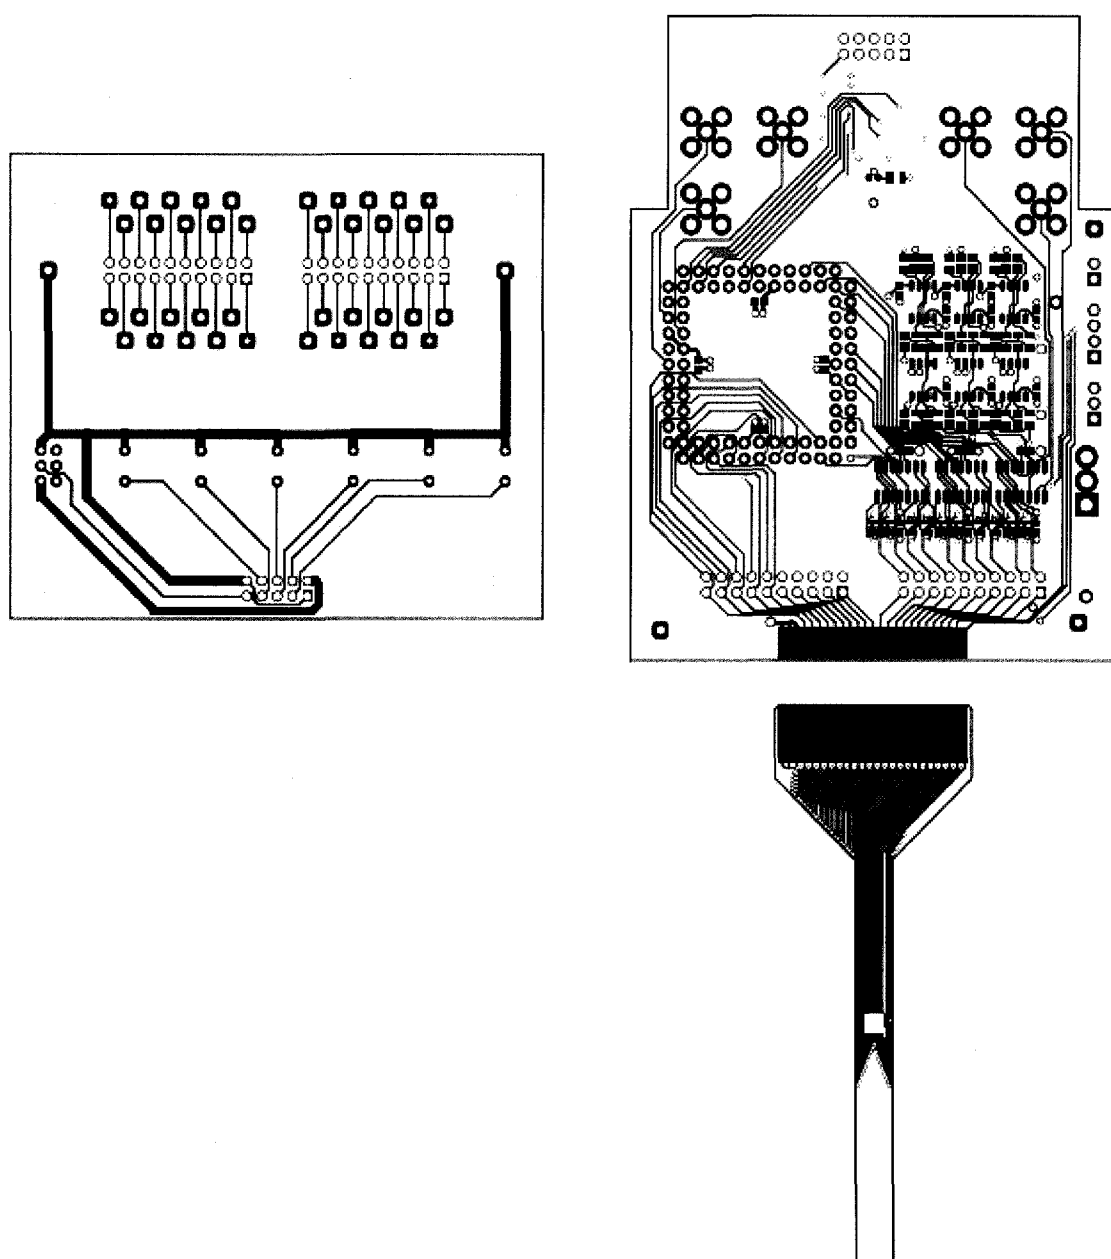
Le dessin de masque du circuit imprimé (vue verso)
